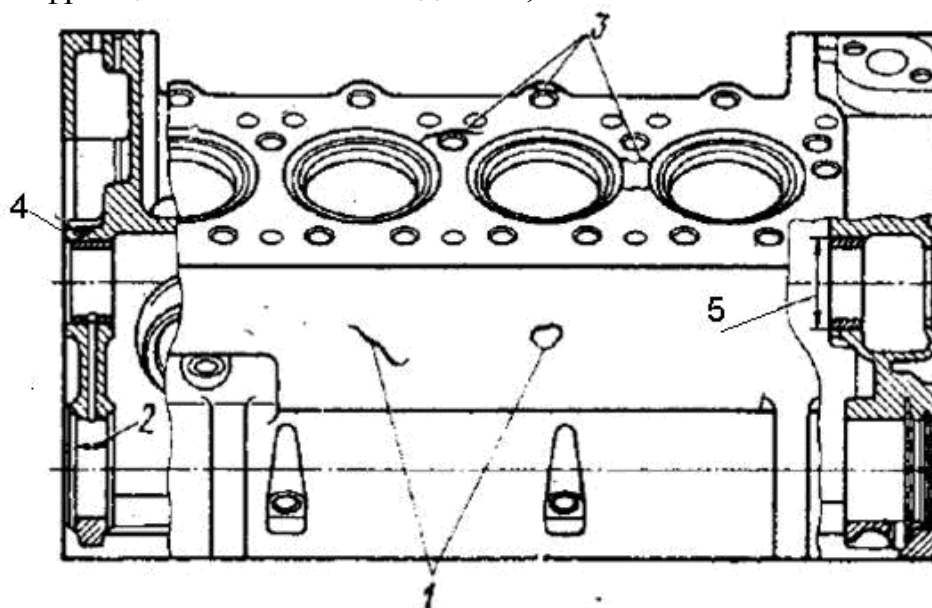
Основные дефекты блока цилиндров 1- пробойны на стенках рубашки охлаждения или картера; 2- износ торцов первого коренного подшипника; 3- трещины и отколы; 4 - износ отверстий во втулках под опорные шейки распределительного вала, 5- износ отверстий под втулки распределительного вала.
